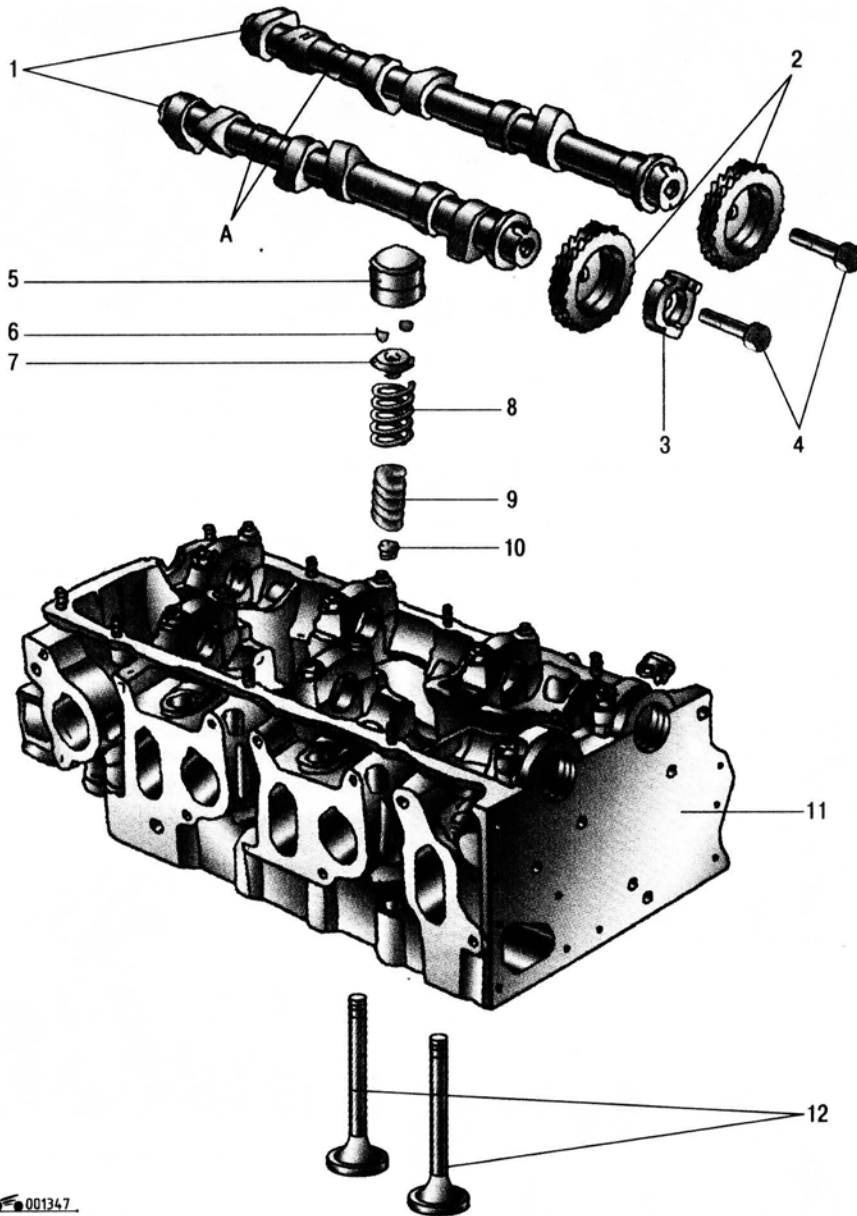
Головка блока цилиндров и механизм клапанов: 1 – распределительные валы; 2 – звездочки распределительных валов; 3 – муфта привода распределителя зажигания; 4 – болты крепления звездочек распределительных валов; 5 – гидравлический толкатель; 6 – сухари клапана; 7 – верхняя тарелка пружин; 8 – наружная пружина; 9 – внутренняя пружина; 10 – маслосъемный колпачок; 11 – головка блока цилиндров; 12 – клапаны; А – шестигранники под ключ для удерживания от проворачивания распределительных валов при отворачивании или заворачивании болтов крепления звездочек
